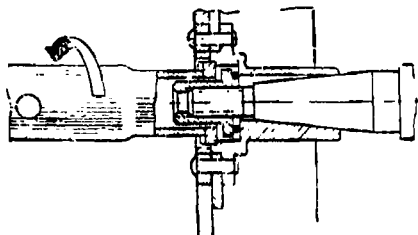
Ослабление затяжки контргайки крепления маховика ключом
